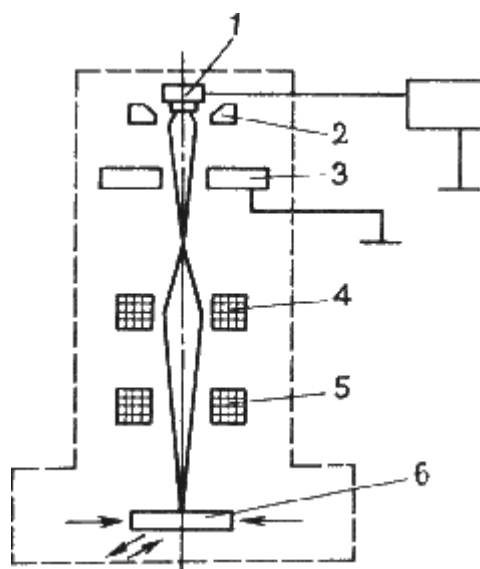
Схема установки для электроннолучевой сварки: 1 – катод электронной пушки; 2 – электрод; 3 – анод; 4 и 5 – отклоняющая магнитная система; 6 – заготовка
